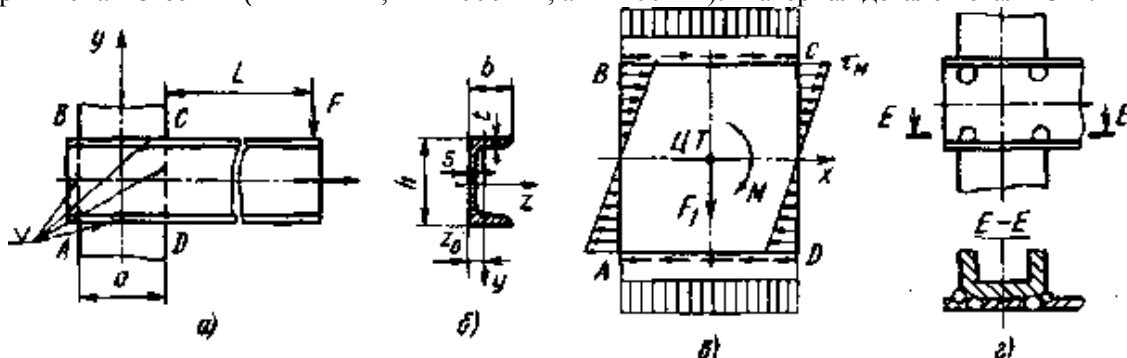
Сварное соединение кронштейна со стойкой:
